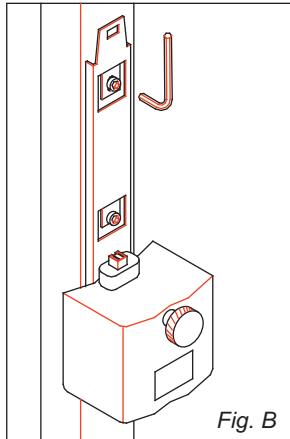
Fig. B - Positionieren Sie die Halterung der Elektronik so, dass die Bohrungen über denen für die eben gelösten Schrauben liegen. Schrauben Sie die Halterung dann gut fest.
